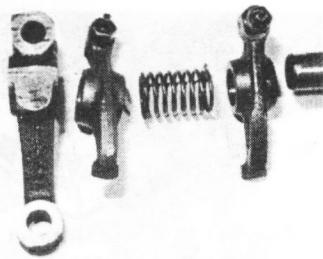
Шатунная передача, разобранная для проверки и очистки
